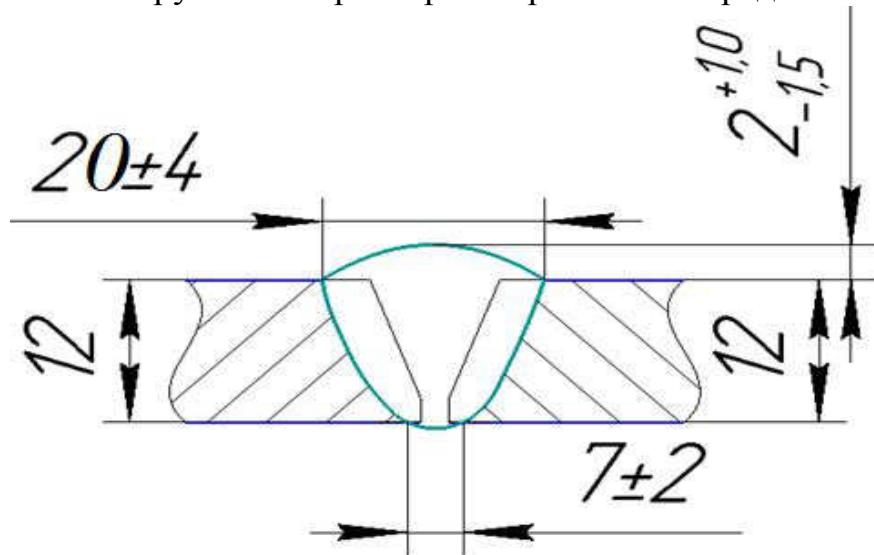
Конструктивные размеры сварного шва
